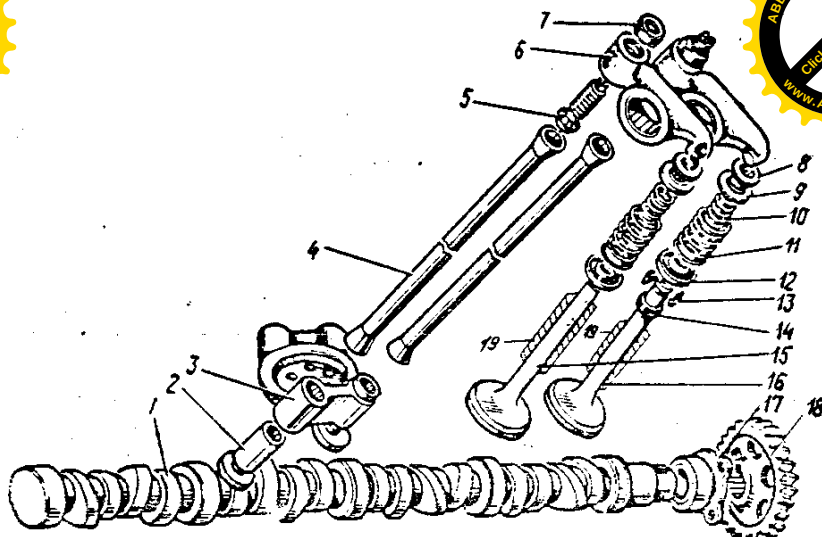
Деталі клапанного механізму газорозподілу: 1 – розподільний вал; 2 – штовхач; 3 – напрямна втулка штовхача; 4 – штанга; 5 – регулювальний болт (гвинт); 6 – коромисло; 7 – контргайка регулювального болта; 8 – втулка; 9 – тарілка пружини; 10 – пружина внутрішня; 11 – пружина зовнішня; 12 – шайба; 13 – сухарики; 14 – манжета; 15 – клапан впускний; 16 – клапан випускний; 17 – упорний фланець; 18 – шестірня розподільного вала; 19 – напрямна втулка клапана
